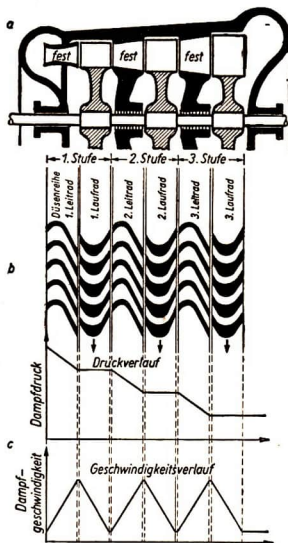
Gleichdruckturbine mit drei Druckstufen. Der Druck sinkt in den Laufrädern von Stufe zu Stufe, ist aber in jeder Stufe konstant. Bedeutung der Teilbilder wie in Abb. 285
